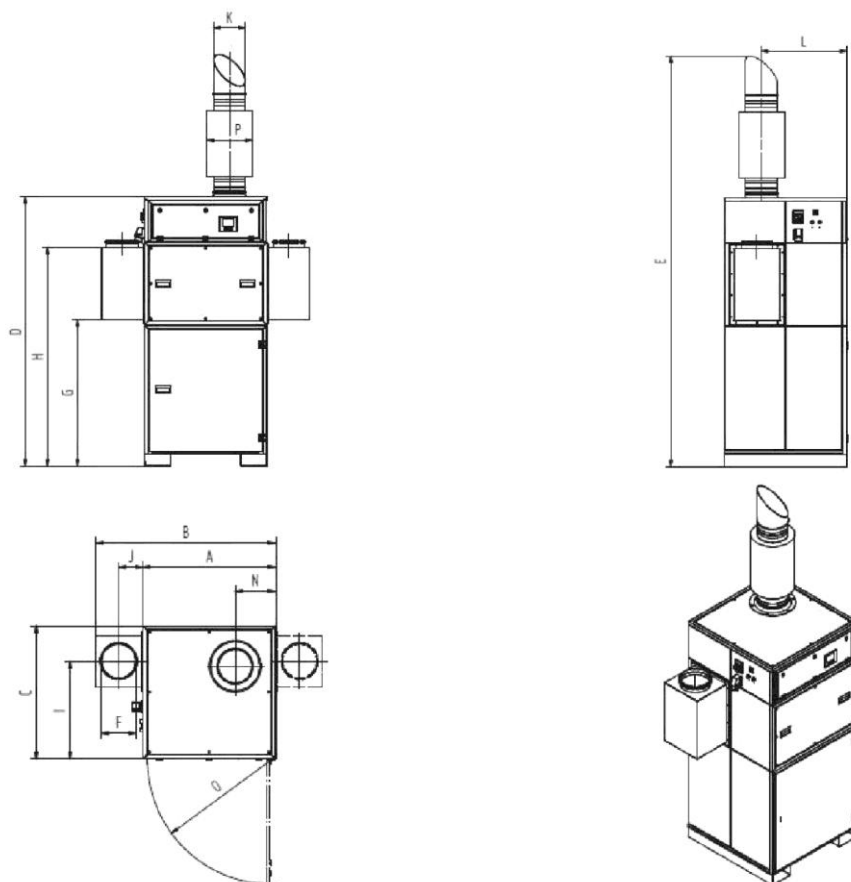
Габаритный чертеж 3520, 3710, 3715, 3720, 322014
